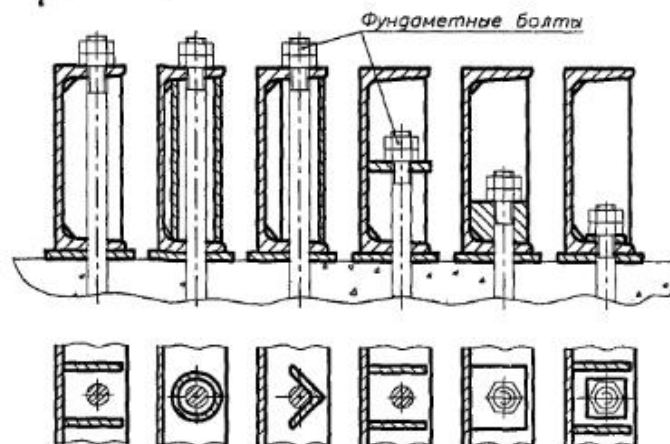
Варианты установки в раме фундаментных болтов
